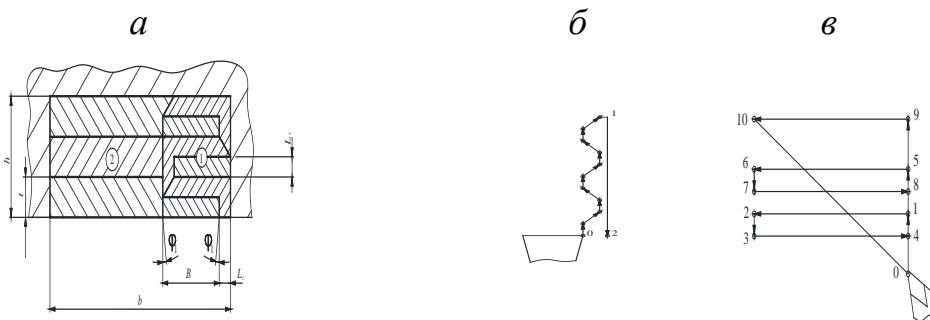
Схема (а) и циклы (б, в) обработки закрытой поверхности вращения (канавки или проточки) прорезным и проходным упорным резцами
